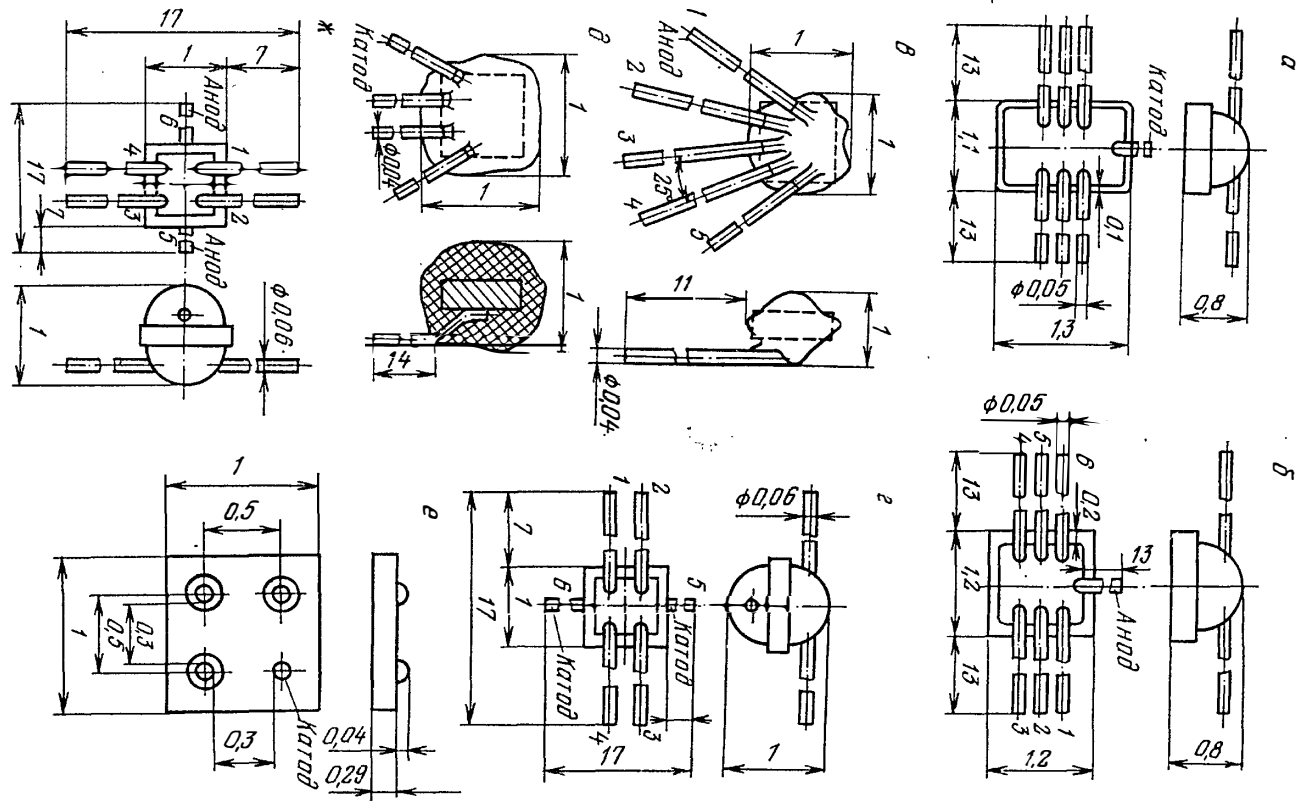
Габаритные чертежи бескорпусных диодных матриц типов:
